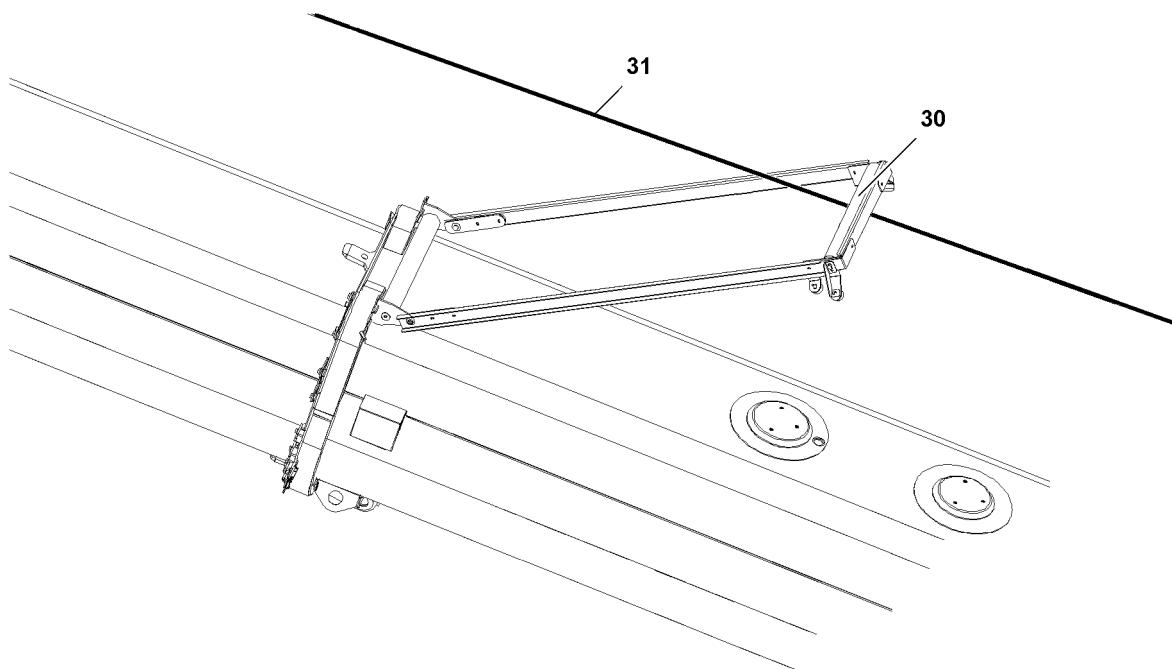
Recorrido del cable de elevación debajo del estribo del cable de elevación 30
